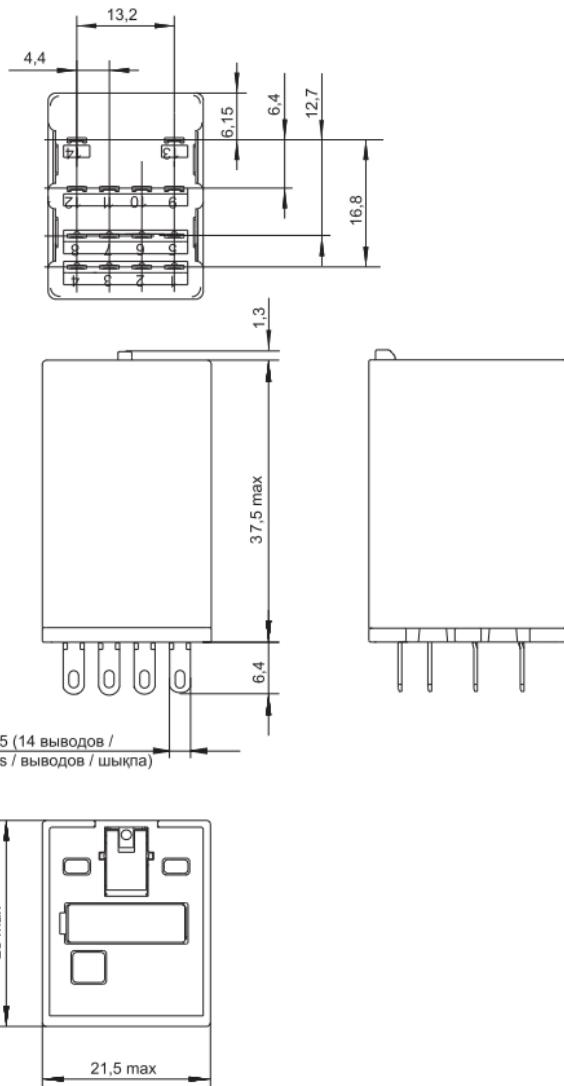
Габаритные и установочные размеры реле / Figure 1 – Overall and mounting dimensions of the relay / 1 сурет – Реленің габариттік және орнату өлшемдері
